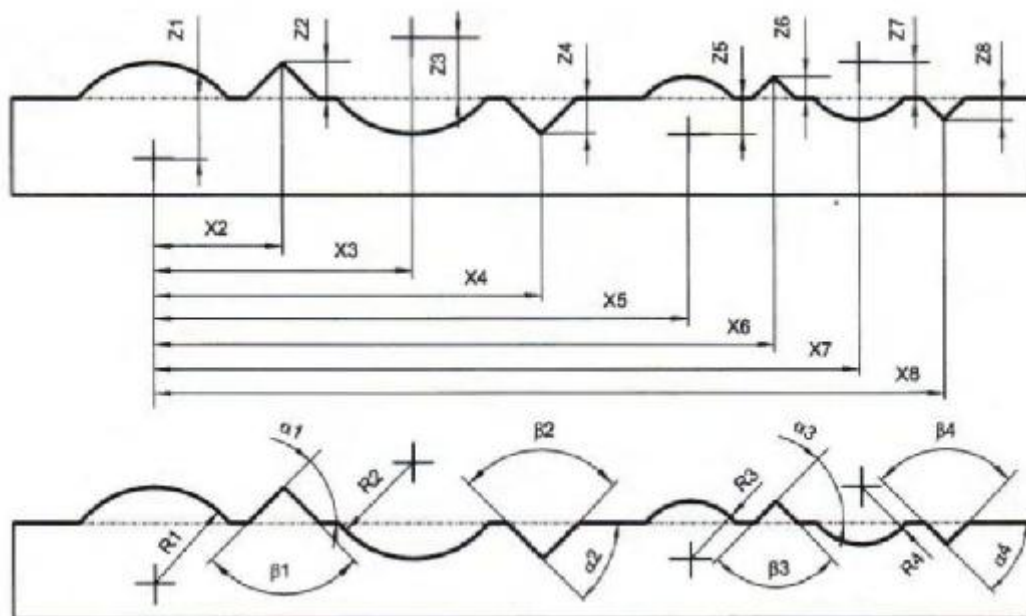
Схема мер для поверки приборов для измерений контура поверхности KN 100
